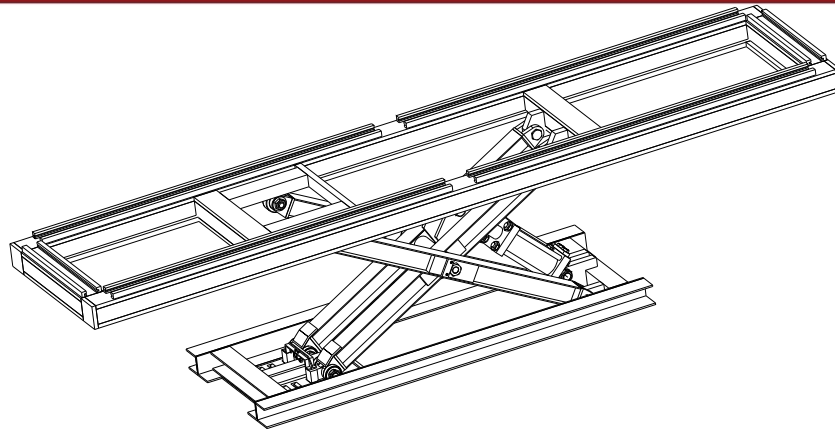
ELEVADOR HIDRÁULICO DE TIJERA
